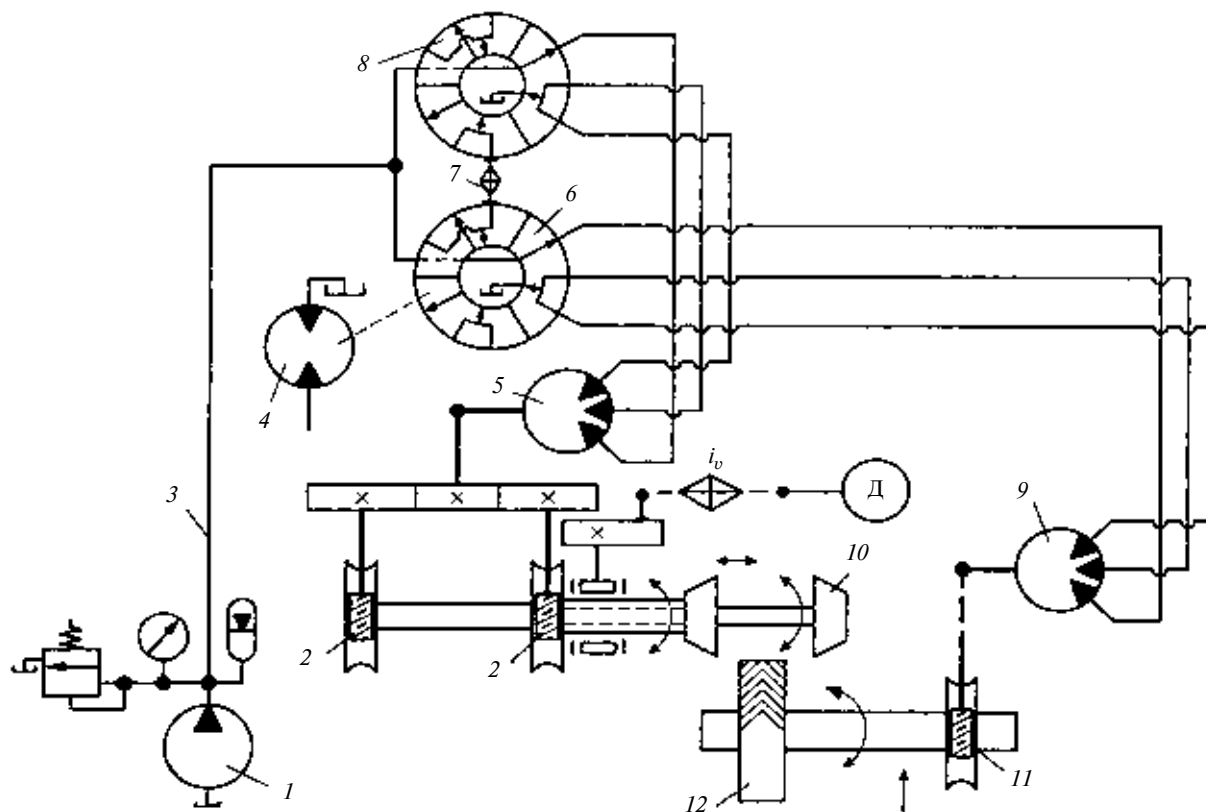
Структурная схема зубодолбежного станка с внутренними гидравлическими связями для нарезания шевронных зубчатых колес:
